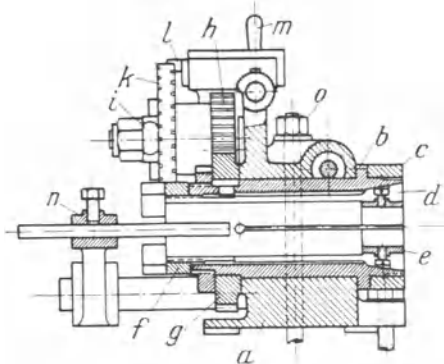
Doppelte Teilvorrichtung für Fräsmaschinen.
